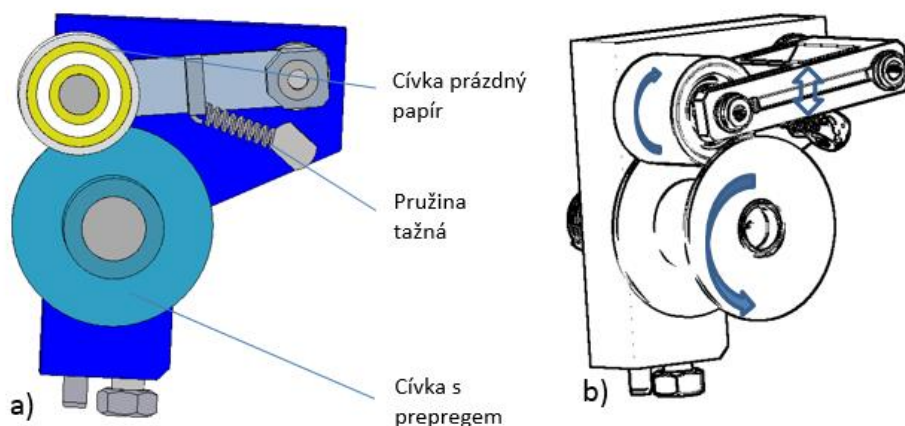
Mechanismus a) Počínající uvolňování pásky b) Zacuchání pásky vlivem výrazné změny převodu navíjecího mechanismu
